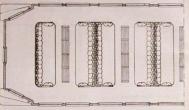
Pianta del tipo di vagone proposto dall'autore.
